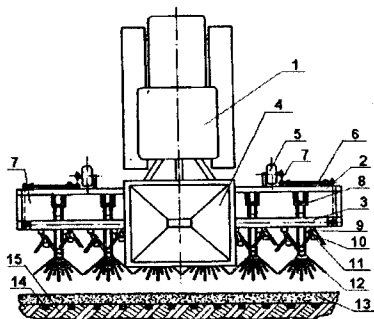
Агрегат с машиной МВВ-4 для локального внесения удобрений совместно с предпосевной обработкой почвы. Конструктивная схема: 1 - трактор; 2 - культиватор КРН - 4, 2; 3 - распределительно-высевающая система; 4 - бункер; 5 - опорное колесо культиватора; 6 - привод РВС; 7 - цепные передачи; 8 - секция культиватора; 9 - приемная камера удобрений; 10 - тукопровод; 11 - подкормочный нож; 12 - борона культиватора; 13 - взрыхленная выровненная почва; 14 - лента минеральных удобрений; 15 - почва после вспашки.
